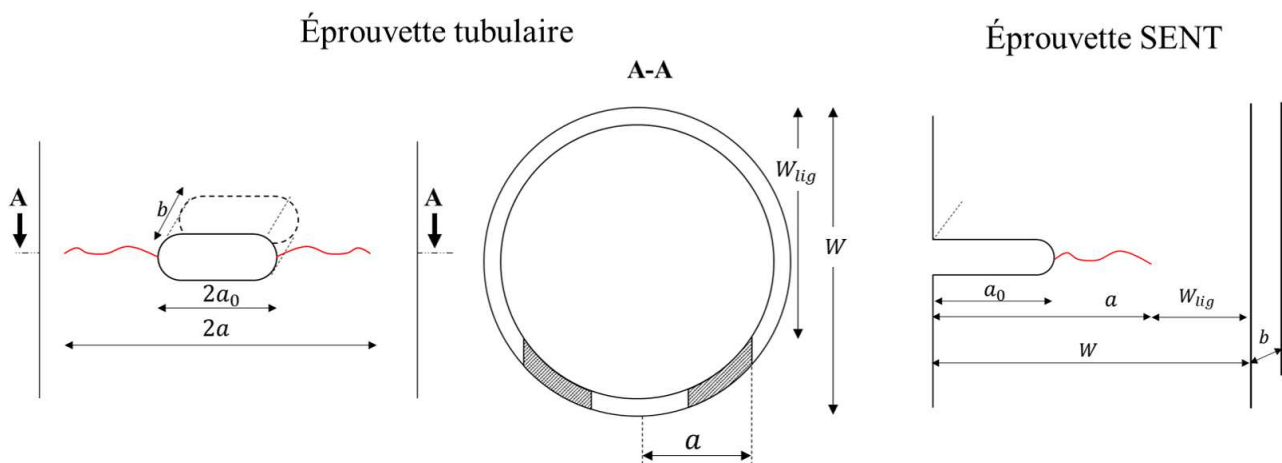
Dimensions caractéristiques des éprouvettes
